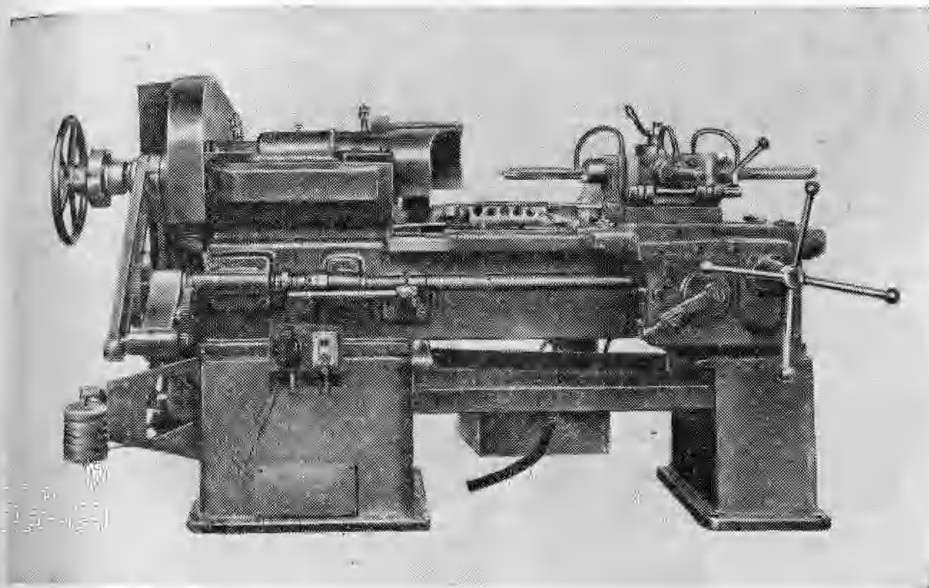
Токарно-многолезцовый полуавтомат мод. 1730, диаметр изделия 300 мм (завод „Красный пролетарий“).
